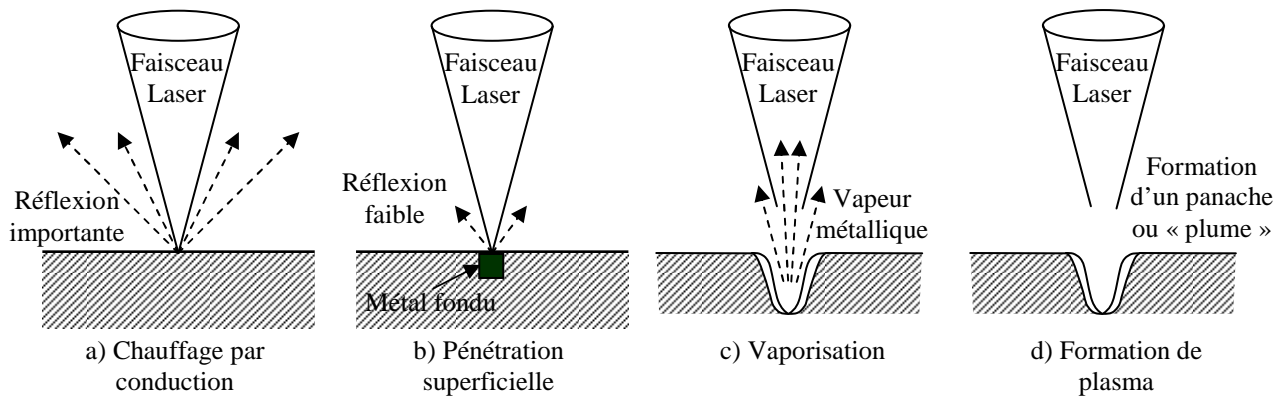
Procédé de soudage par laser YAG [Paradis, 2005]
